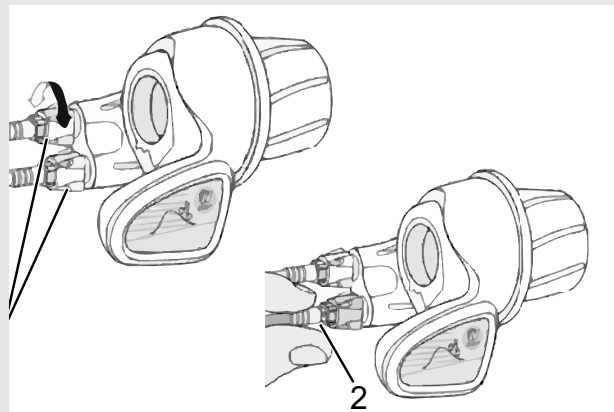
Slutmuffer (2) på to alternative udførelser (A eller B) af et gearskit med to kabler på baggafflen (1)
